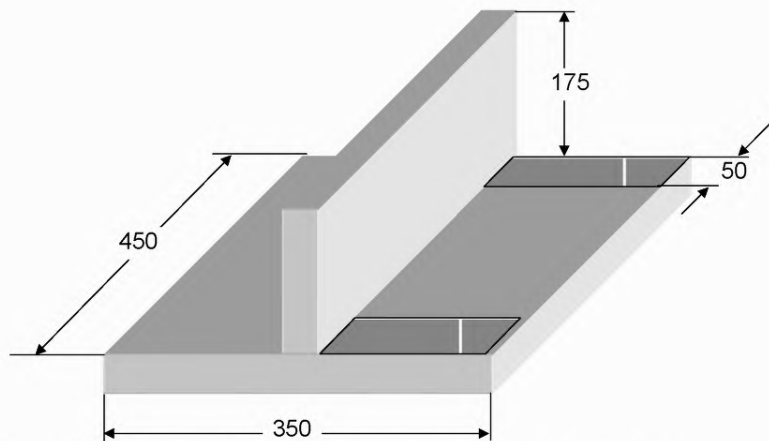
Контрольные сварные соединения типов ТБ; TV; TX.
